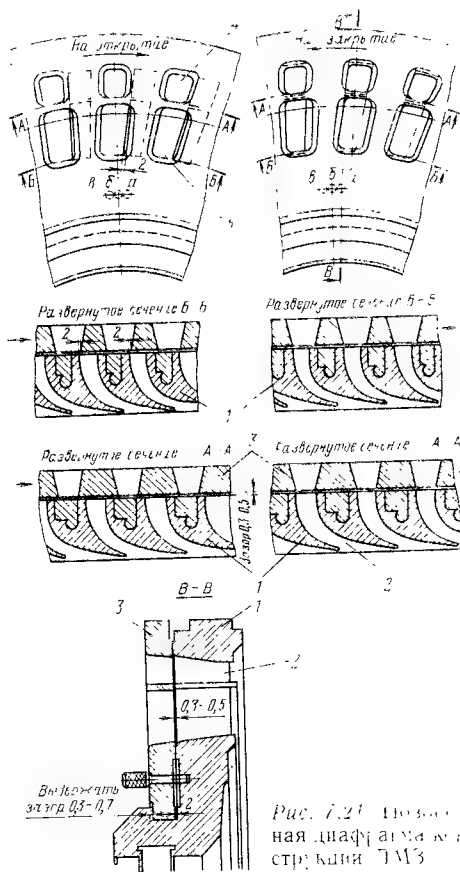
Подшипниковая диафрагма конструкции ТМЗ
